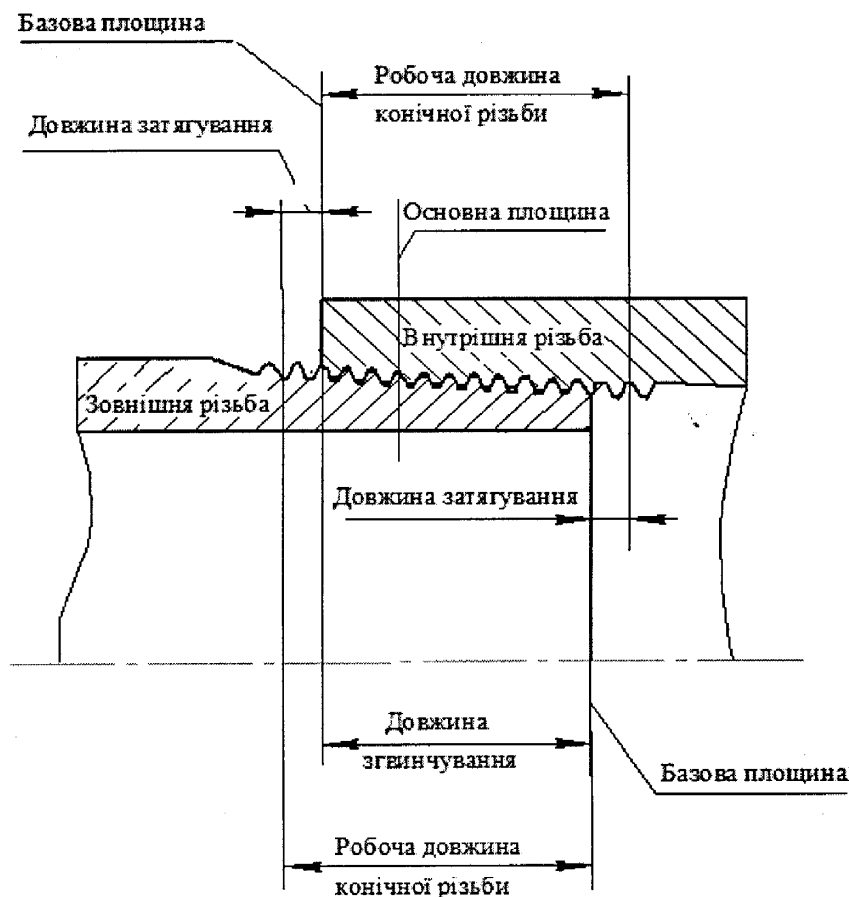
Робочі та базові елементи конічної різьби
